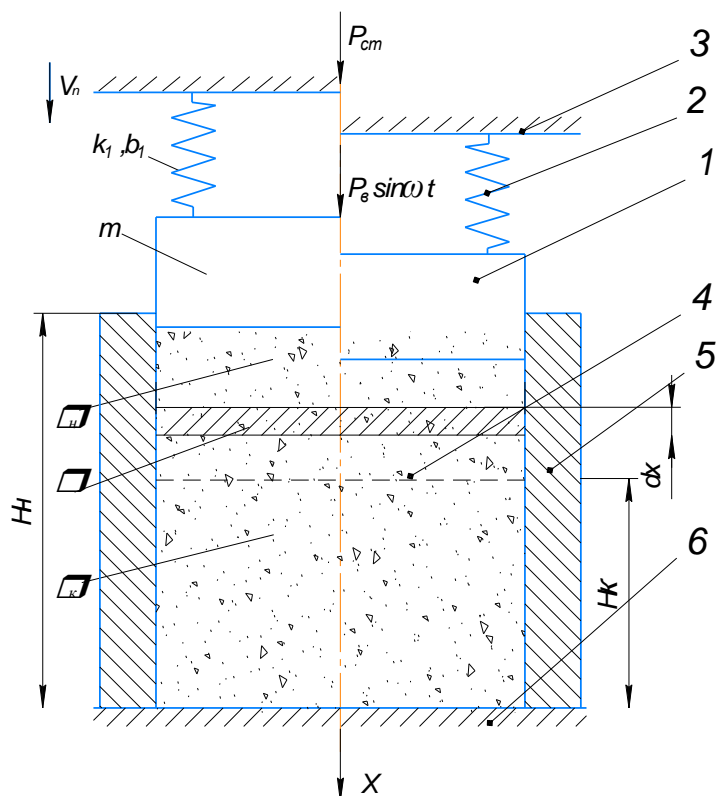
Схема процесу деформування порошкової заготовки (1 – пуансон; 2 – пружний амортизатор; 3 – натискна плита; 4 – порошкова заготовка; 5 – форма; 6 – основа
